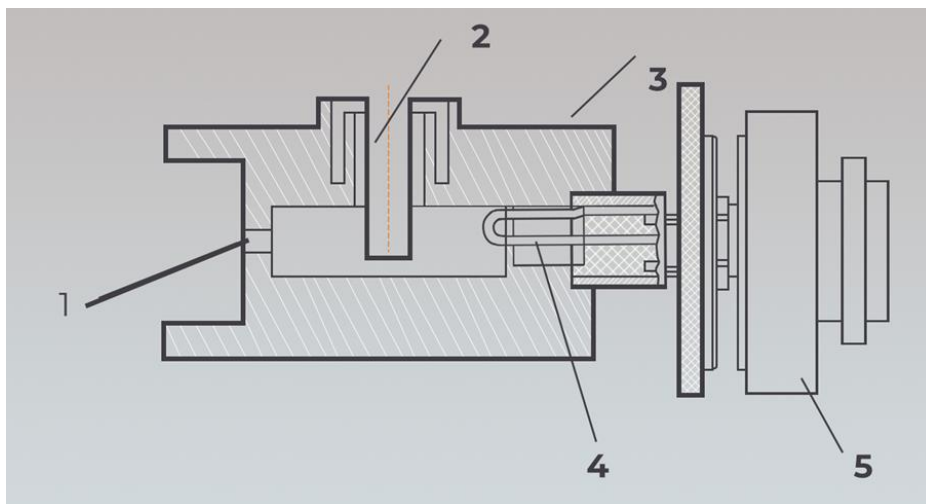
Конструкция объемного цилиндрического резонатора лазера:
